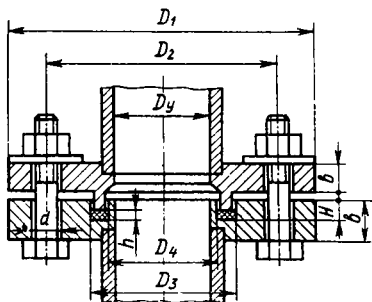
Конструкция соединения с несимметричными фланцами и фторопластовым уплотнителем
